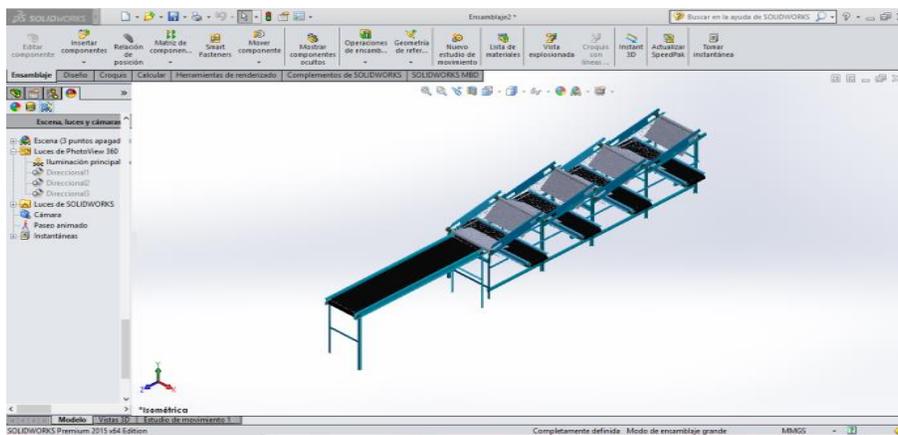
Diseño de la máquina completa ensamblada y en posición de instalación
